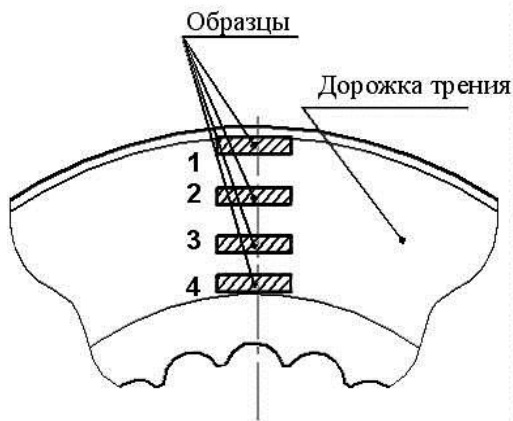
Схема вырезки образцов на поверхности трения тормозного диска
